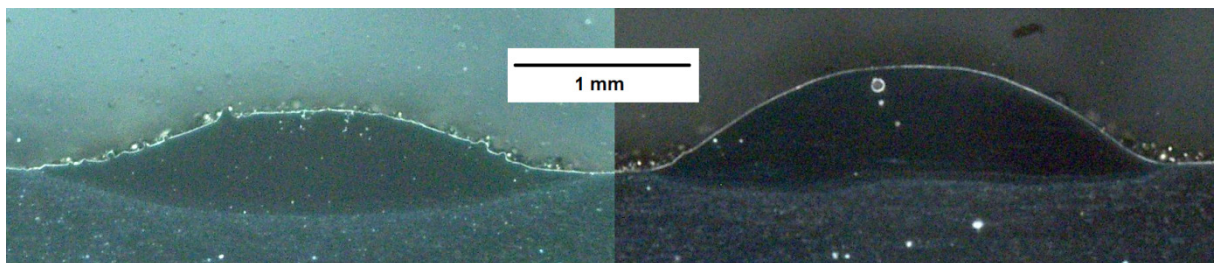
Auftragschweißspur ohne (links) und mit (rechts) Gasdruckminimierung im Querschnitt
